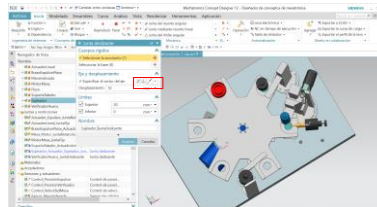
Junta deslizante sujetador, con 10 mm de desplazamiento.
